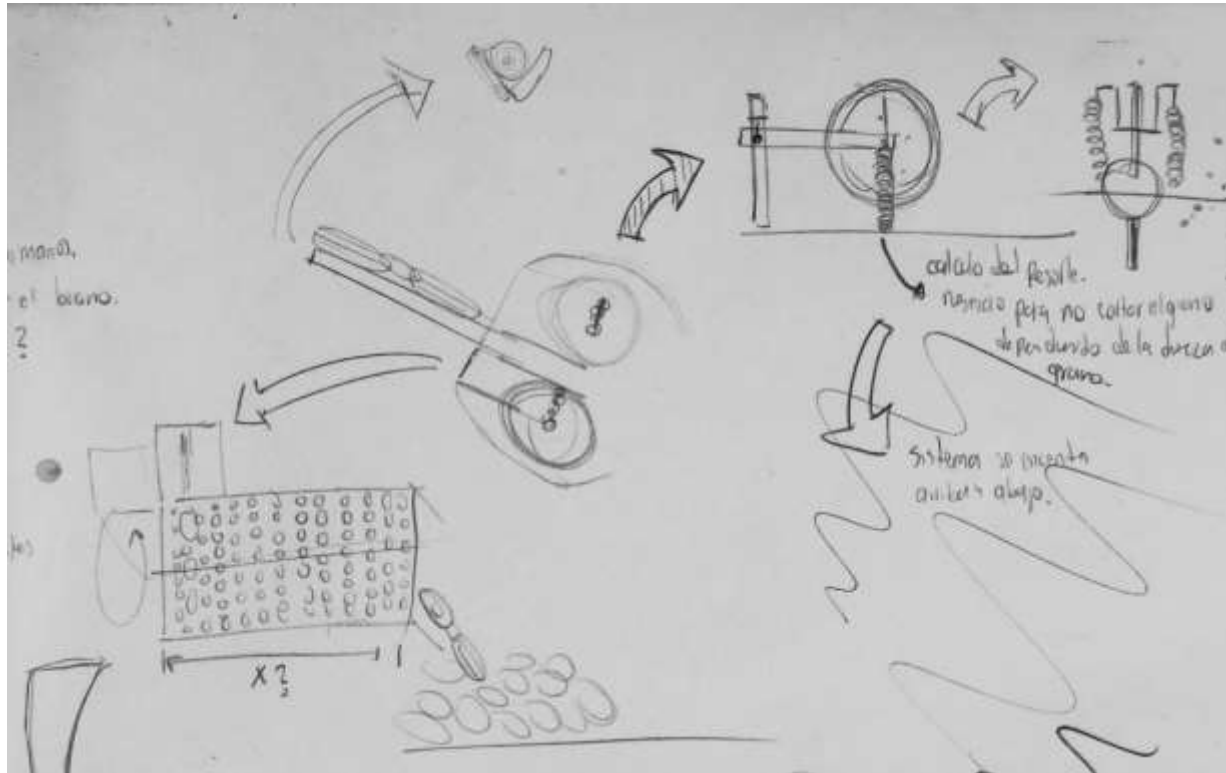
Boceto donde se ilustran algunos detalles de la alternativa.
